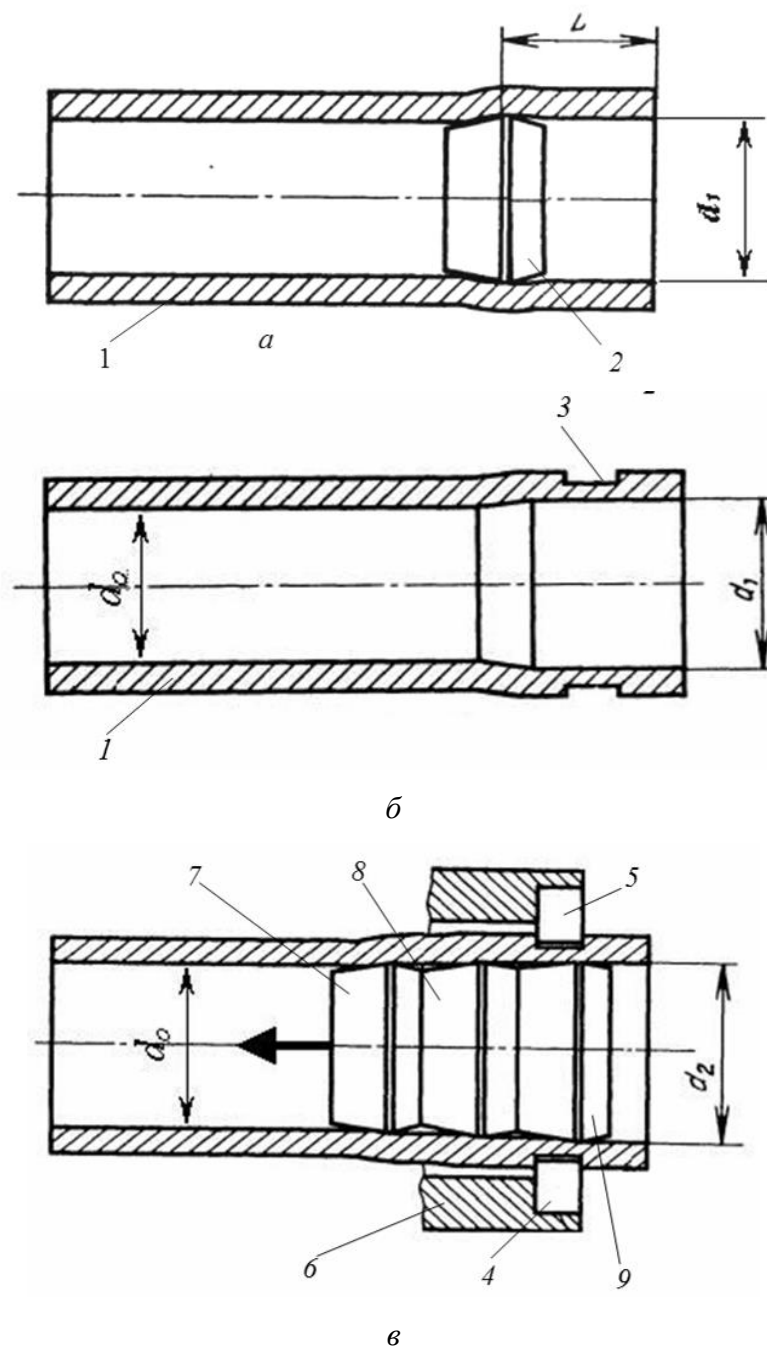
Деформування за схемою розтягнення з попередньою підготовкою бази для закріплення заготовки
